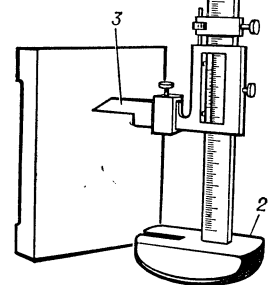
Штангенрейсмас: 1 — штанга; 2 — основание; 3 — чертилка.
